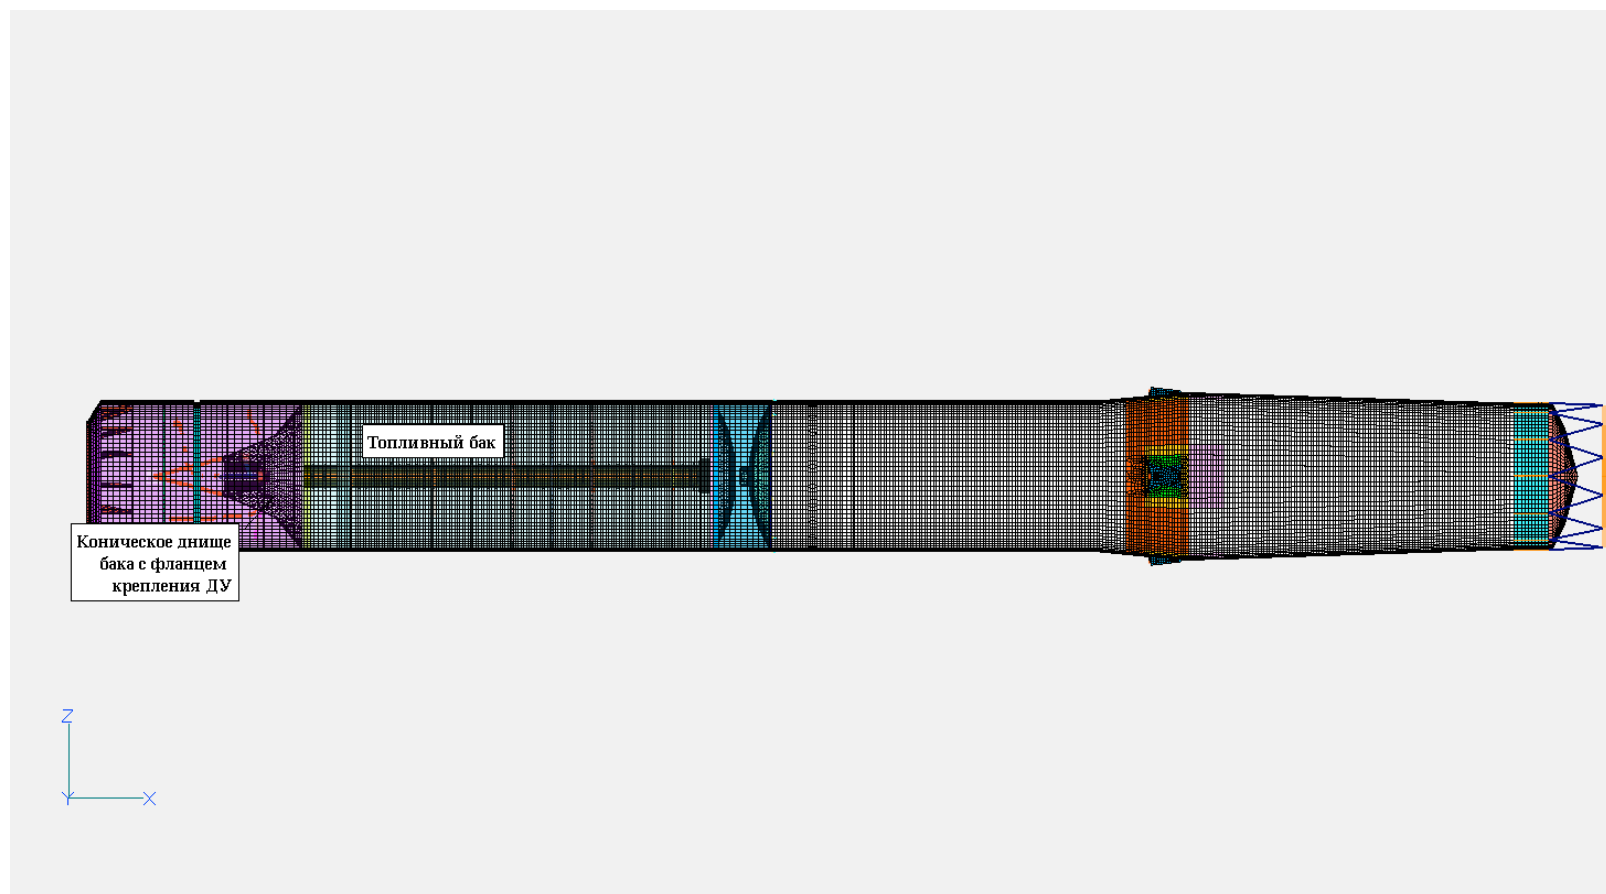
Первая ступень РН: Топливные баки; Крепление двигательной установки
